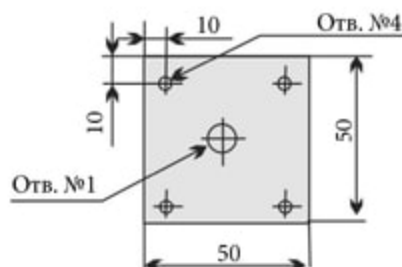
Крышка подшипника (деталь № 3) — 6 шт.
